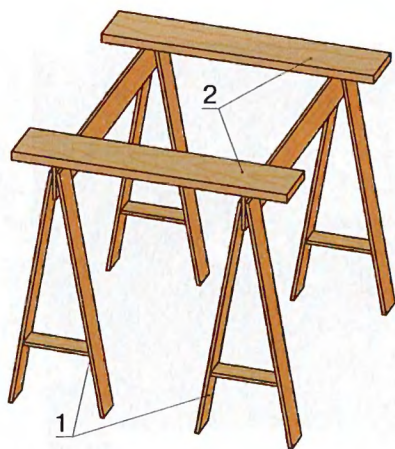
Станина распиловочного станка: 1 — козлы; 2 — доски 50 × 150 мм.
